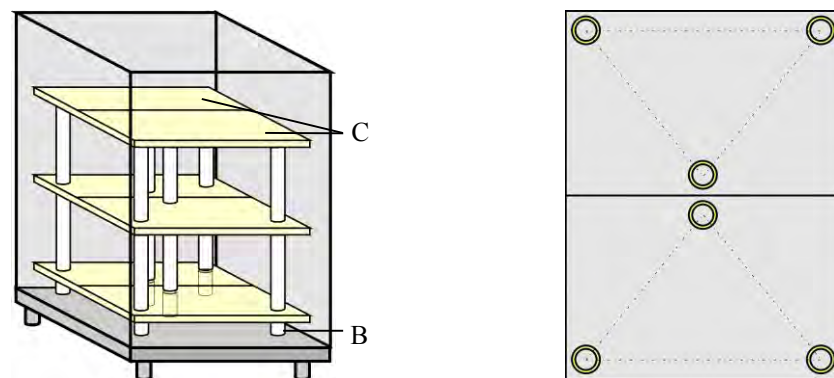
Exemple 1 : Montage de plusieurs plaques de four individuelles sur un même niveau (figure analogue)
